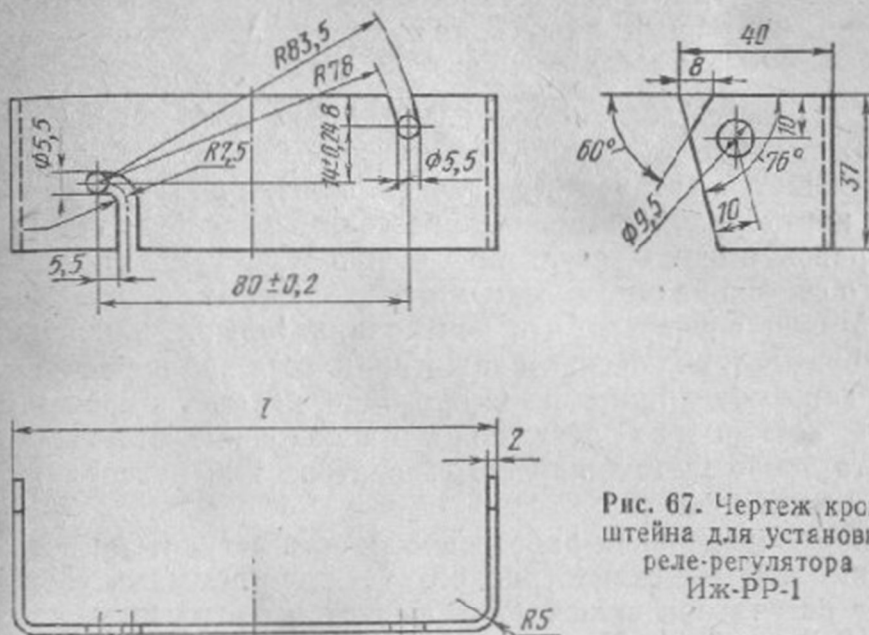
Чертеж кронштейна для установки реле-регулятора Иж-РР-1
